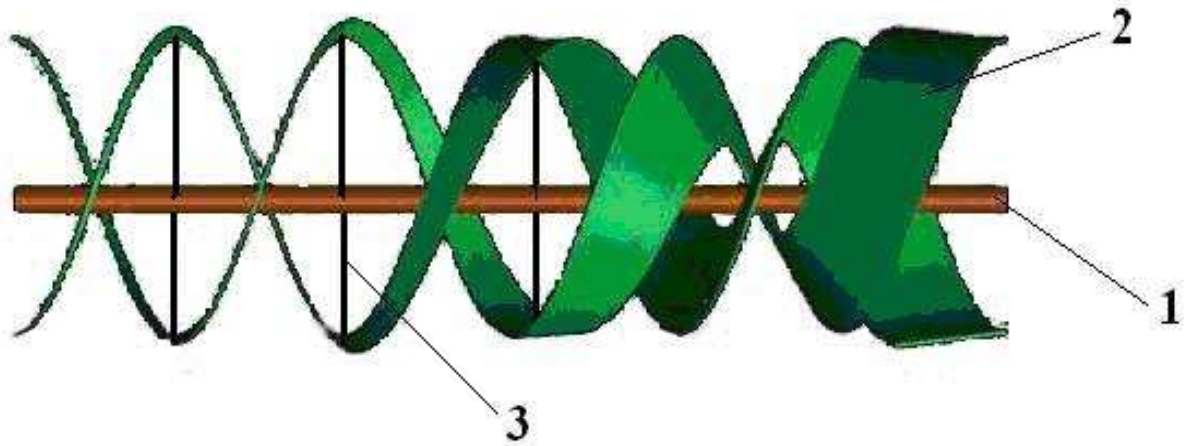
Конструкция фрезы, где 1 – вал; 2 – лента фрезы питателя; 3 – спицы.
